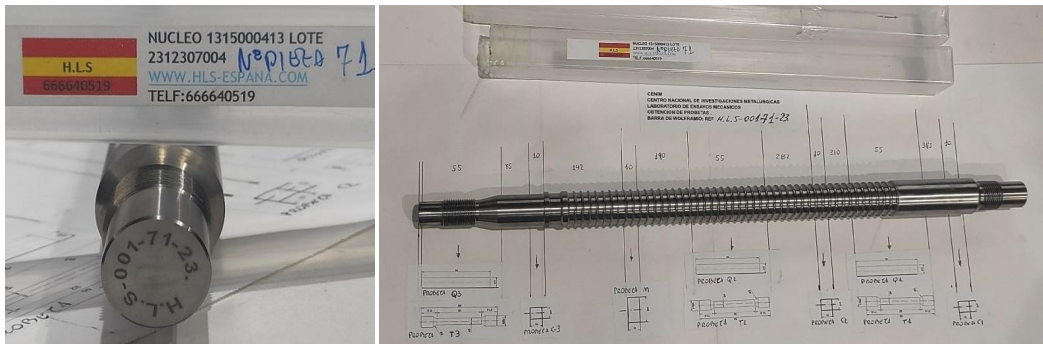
Detalle de barra y plano para extracción de probetas recibidos en el CENIM
